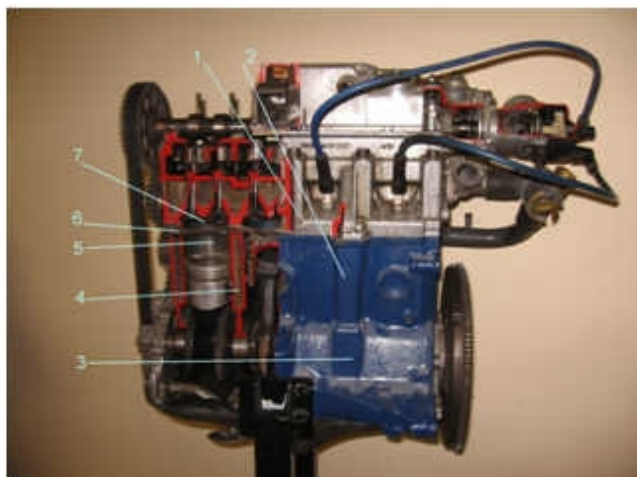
Блок и головка блока цилиндров (справа на двигателе расположен маховик, относящийся к подвижным частям КШМ):
